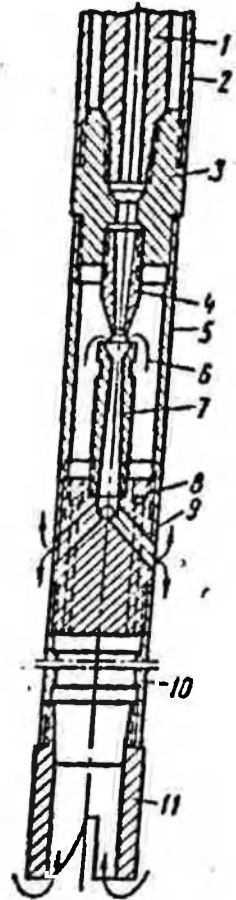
Колонковый снаряд Ф. II. Твердохлебова
